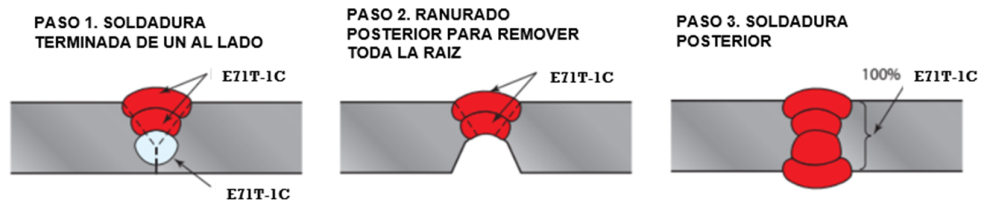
Soldadura de carcasa de la caldera
